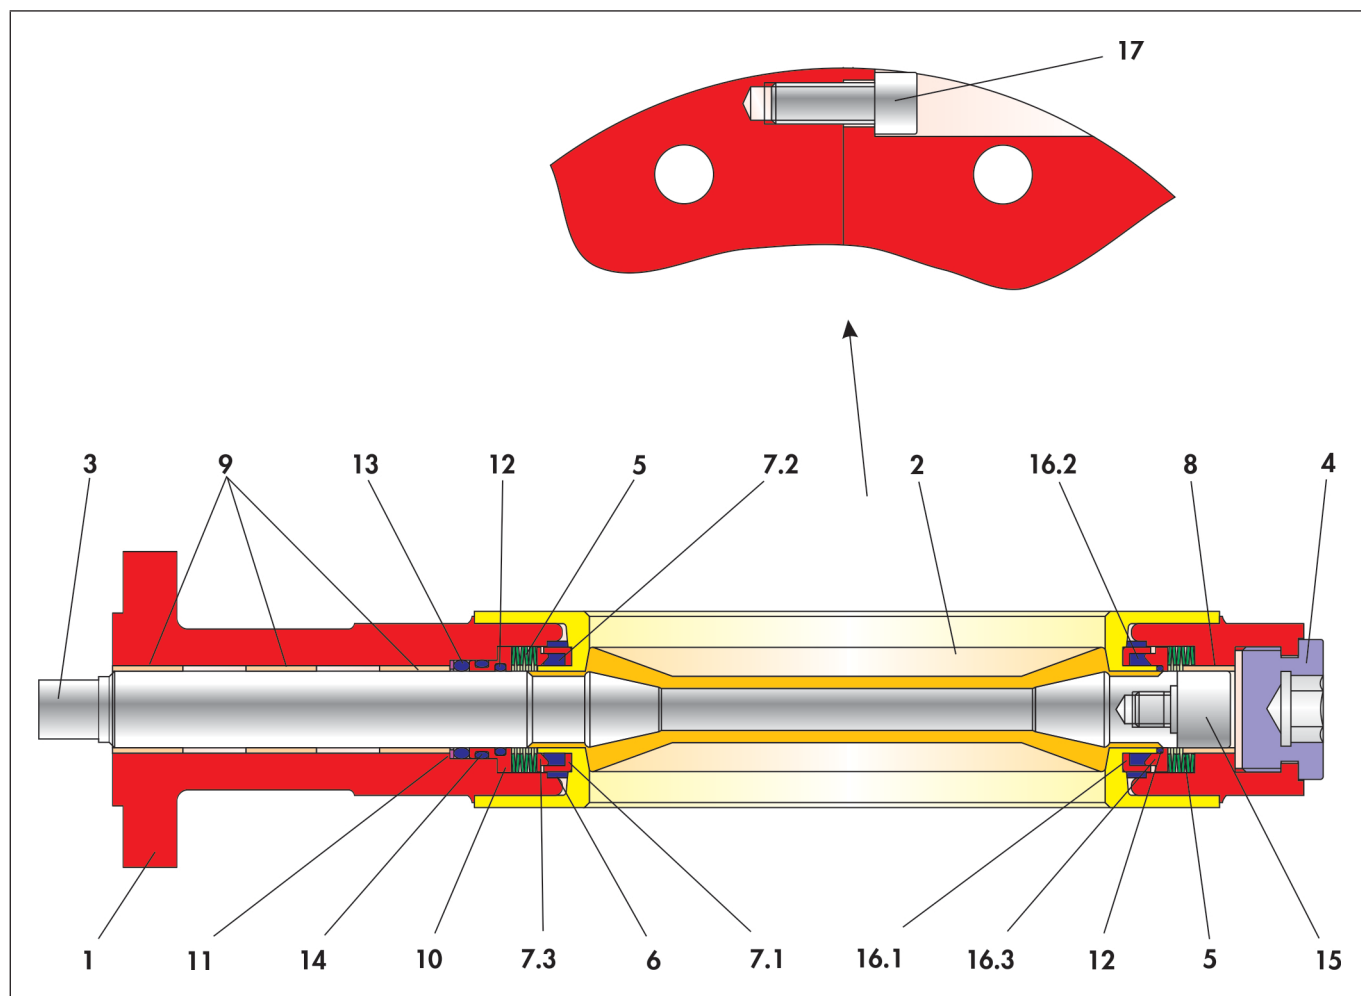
Desenho em corte da válvula borboleta BR 10e
